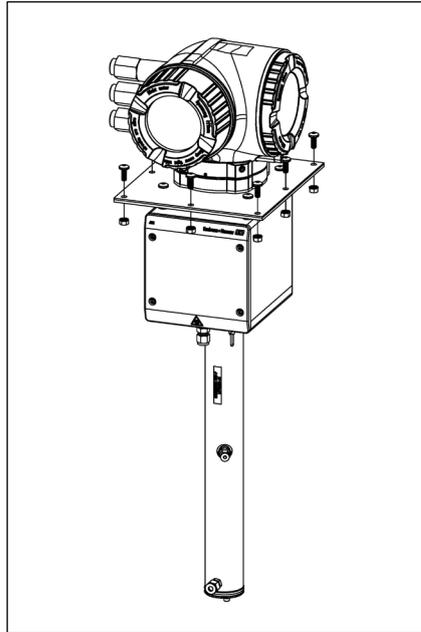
Halterung für Montage auf einem Befestigungsblech und Befestigungsmaterialien
